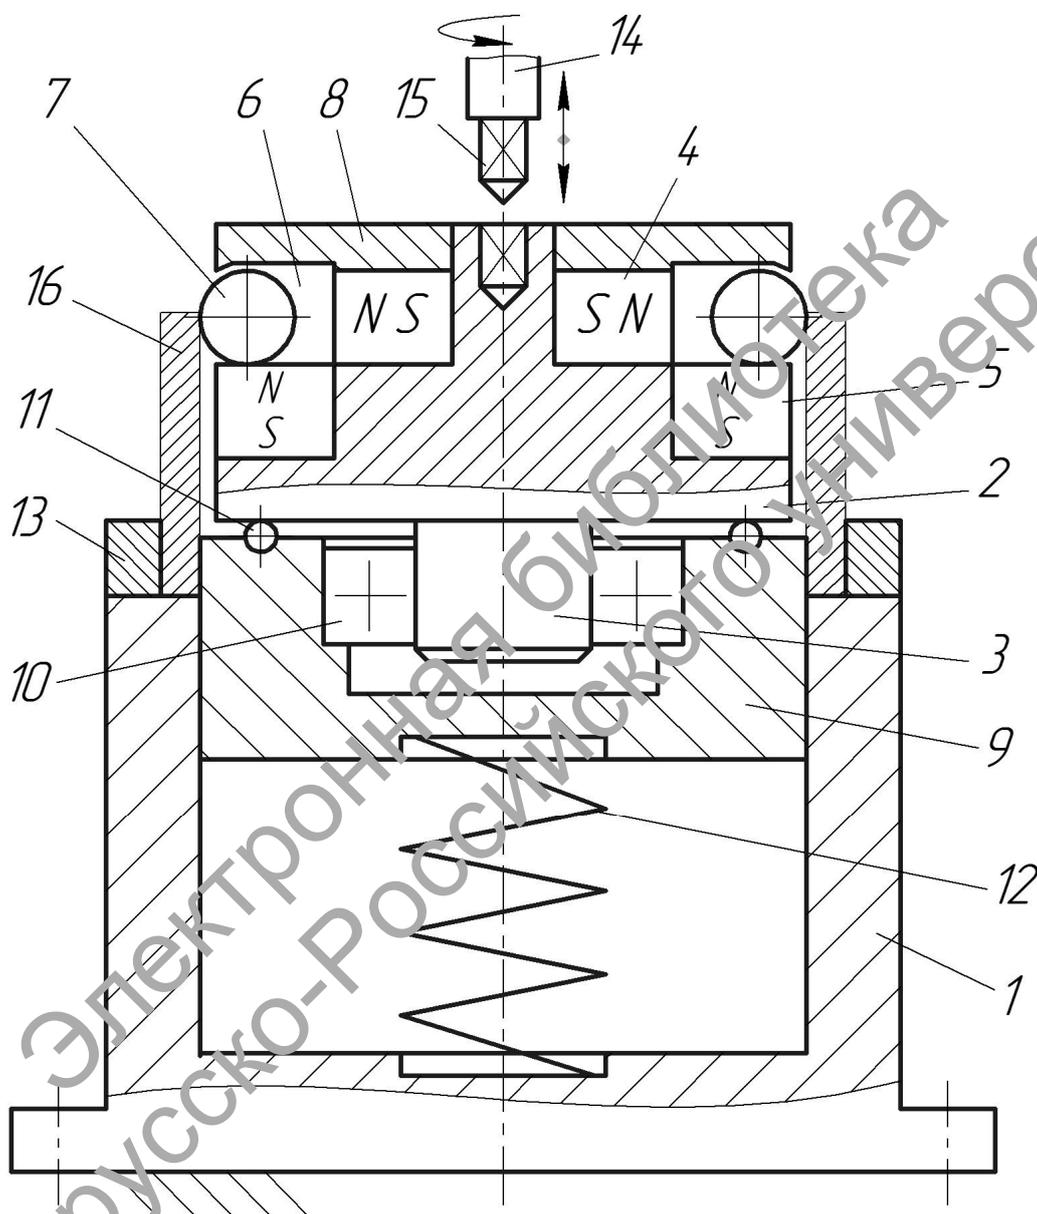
Схема совмещенного магнитно-вибродинамического упрочнения внутренней поверхности втулок на вертикально-сверлильном станке: 1 – цилиндрический корпус; 2 – ротор; 3 – шейка; 4, 5 – источники магнитного поля; 6 – кольцевая камера; 7 – деформирующие шары; 8 – шайба; 9 – плунжер; 10 – подшипник; 11 – шариковые опоры; 12 – пружина; 13 – упругое кольцо; 14 – поводковый центр; 15 – рабочий элемент поводкового центра; 16 – упрочняемая ферромагнитная втулка
